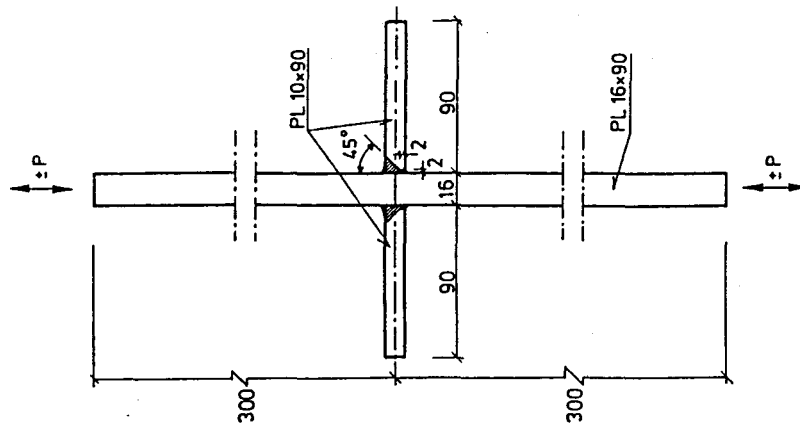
Détails des éléments plaques soudés [AGE97]
